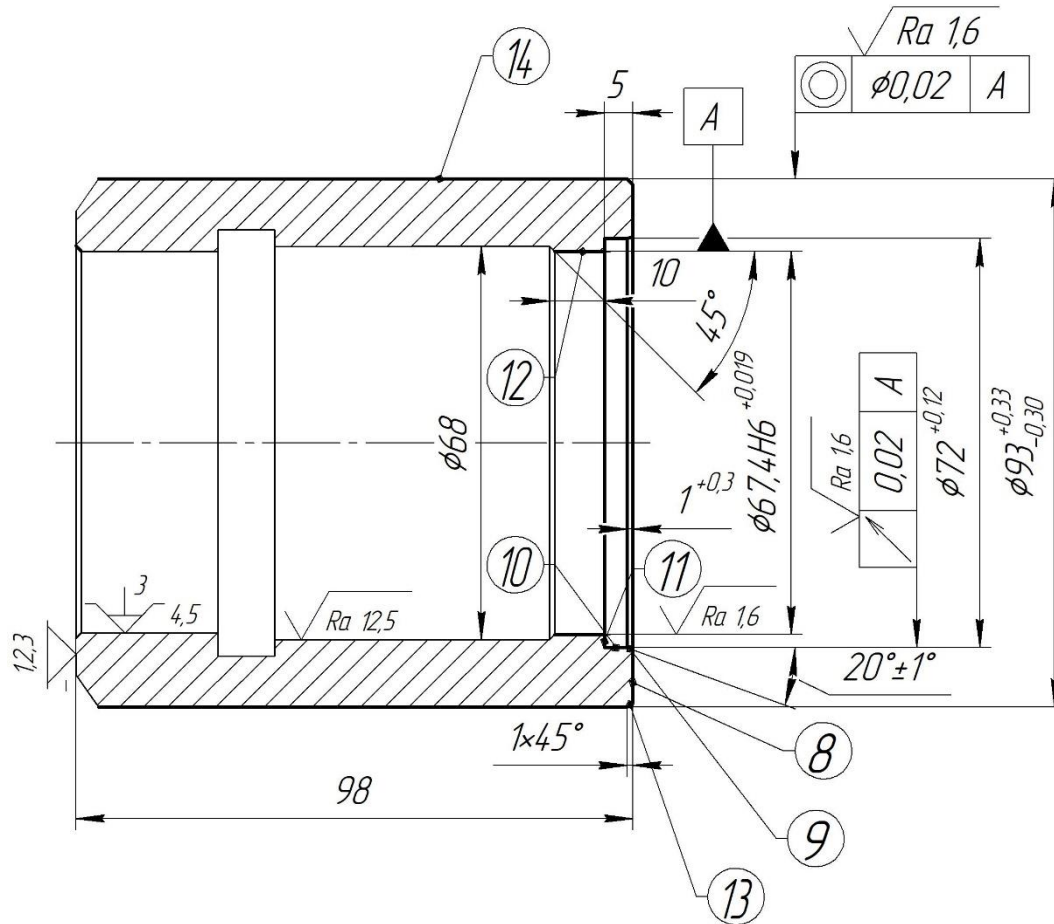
Схема установки заготовки на операції 025 установ Б
